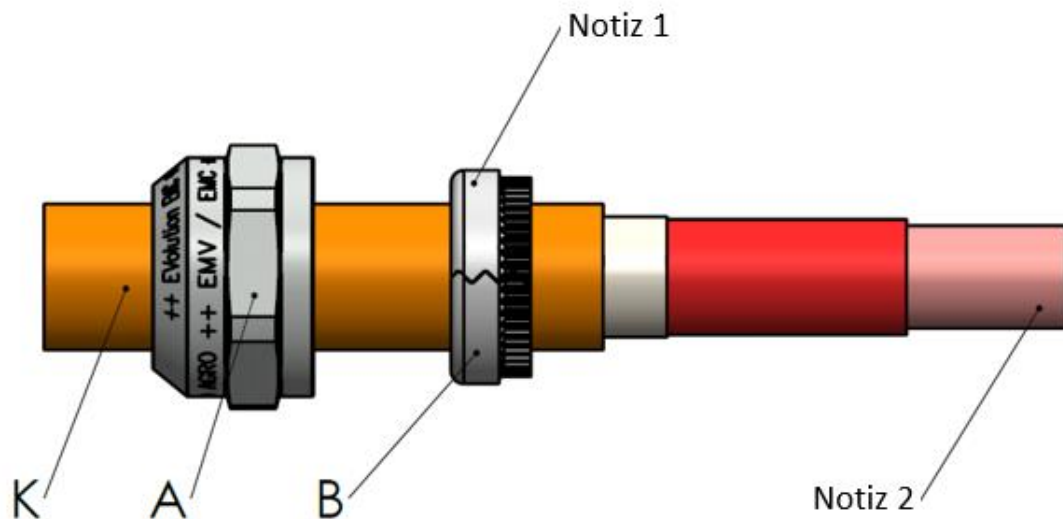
Montaggio della parte superiore e dell'inserto di tenuta
